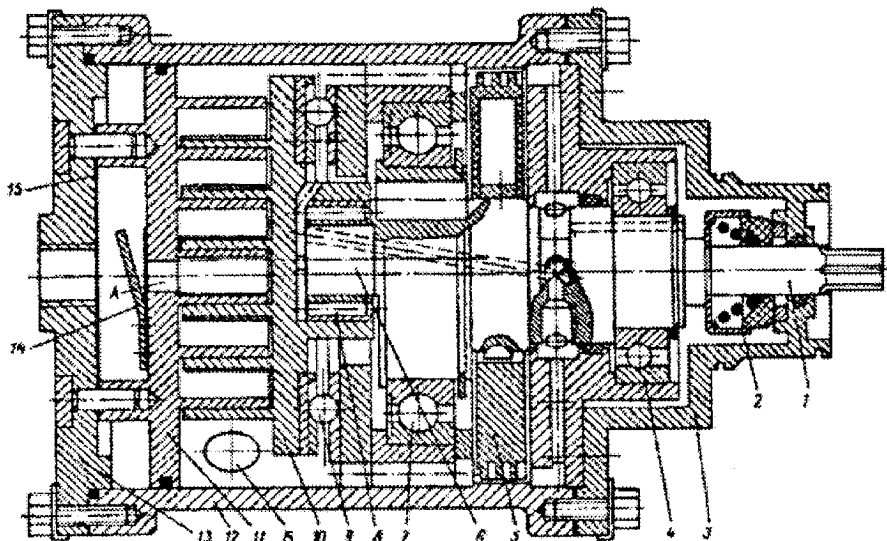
Подовжній розріз спірального компресора: 1 – вал компресора; 2 – сальник; 3 – передня кришка; 4, 7, 8 – підшипники; 5 – противага; 6 – ексцентрик; 9 – кулька протиповоротного пристрою; 10 – рухома спіраль (РСП); 11 – нерухома спіраль (НСП); 12 – корпус компресора; 13 – задня кришка; 14 – обмежувач клапана; 15 – підганяльне кільце.
